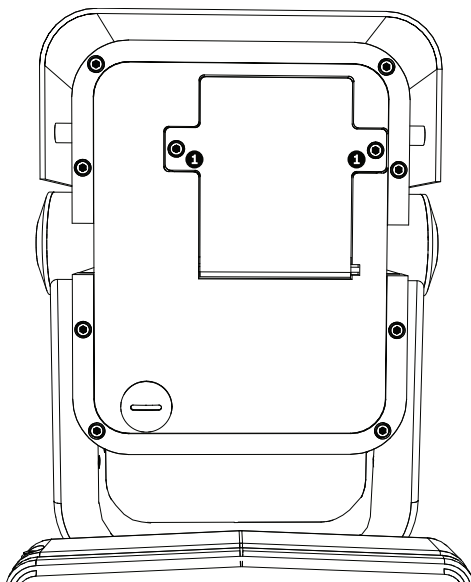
Parte posterior de la carcasa de la cámara con panel de acceso
